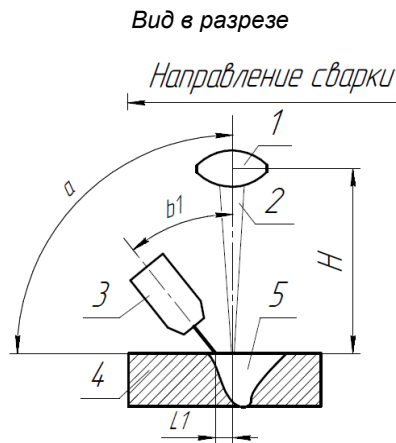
Схема ГЛДС, метод «Гибрид» стыкового сварного соединения в нижнем положении (РА):
